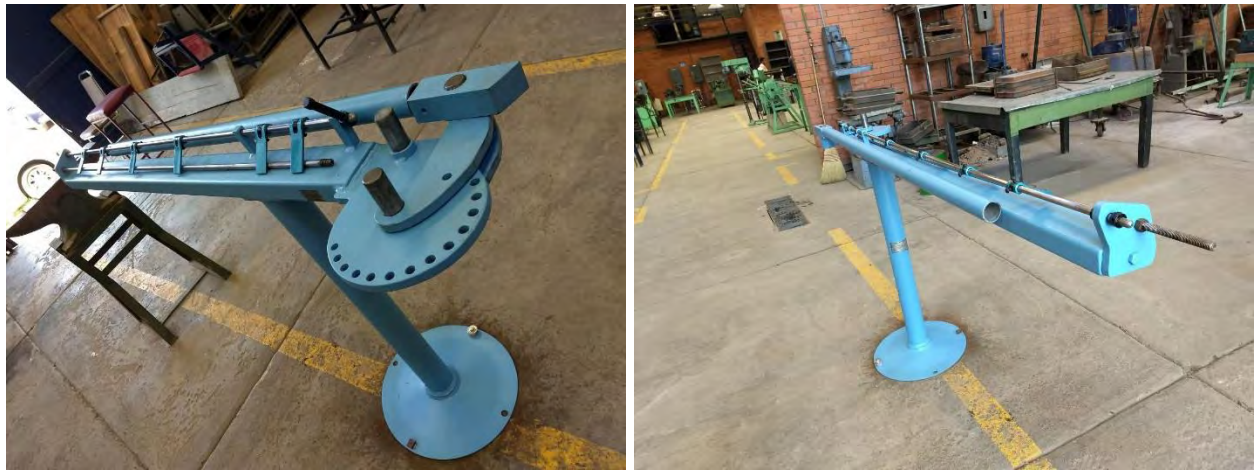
Maquina dobladora de tubos después del baño de pintura con acabado mate.
